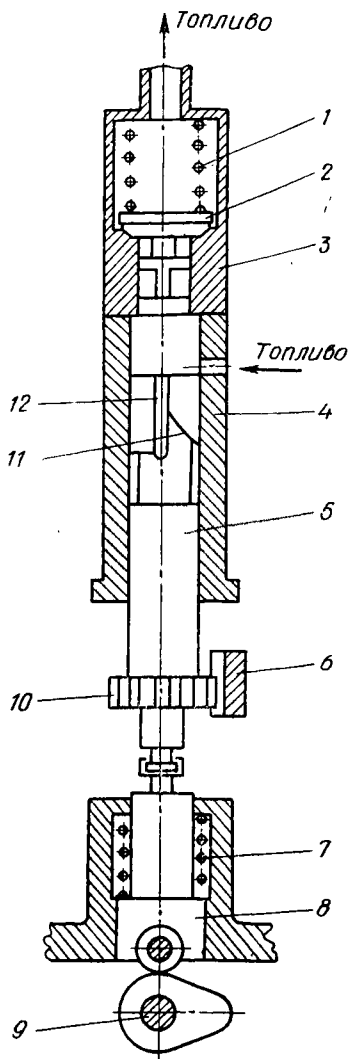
Схема секции топливного насоса высокого давления: 1 — пружина нагнетательного клапана; 2 — нагнетательный клапан; 3 — гнездо клапана; 4 — гильза; 5 — плунжер; 6 — рейка; 7 — возвратная пружина толкателя; 8 — роликовый толкатель; 9 — кулачковый вал привода насоса; 10 — зубчатый венец на нижнем конце плунжера; 11 — винтовая отсечная кромка; 12 — продольная канавка (канал).
